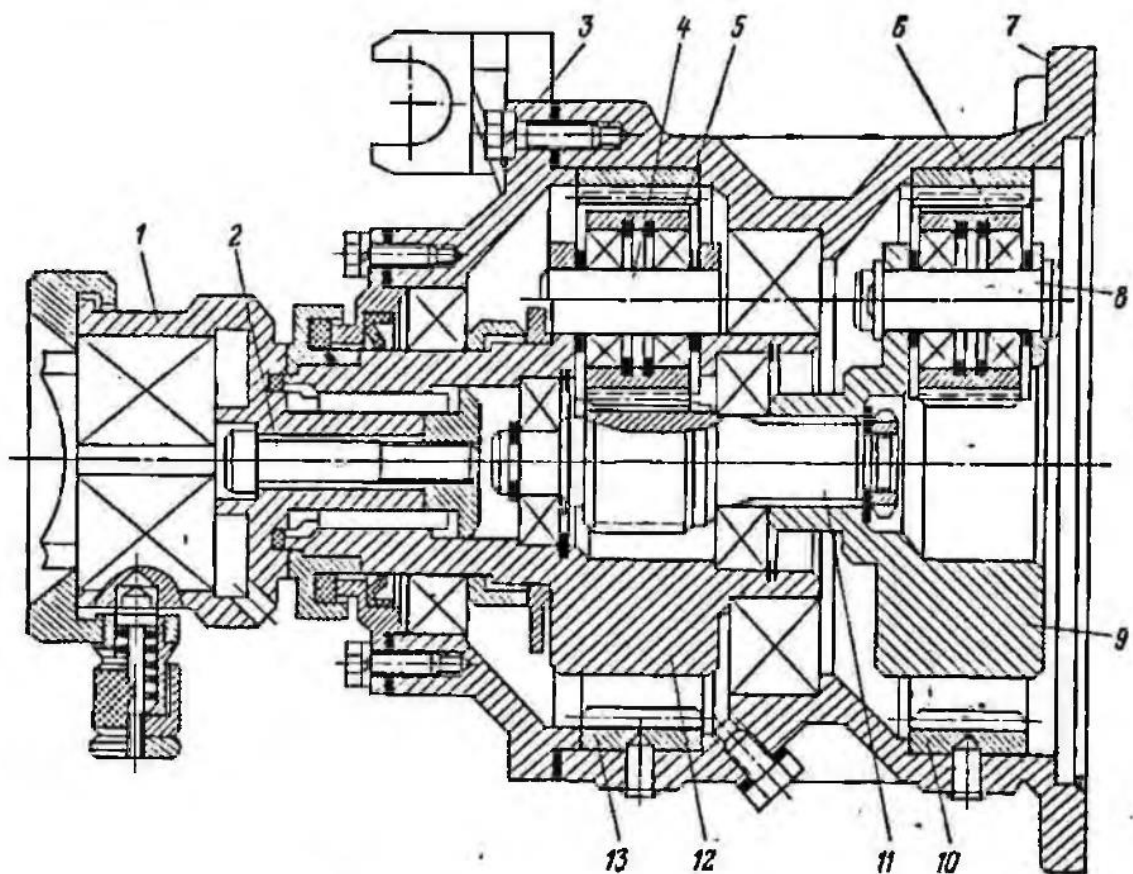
Привод обертача бурового верстата Б15с [2, 7, 12, 19].
